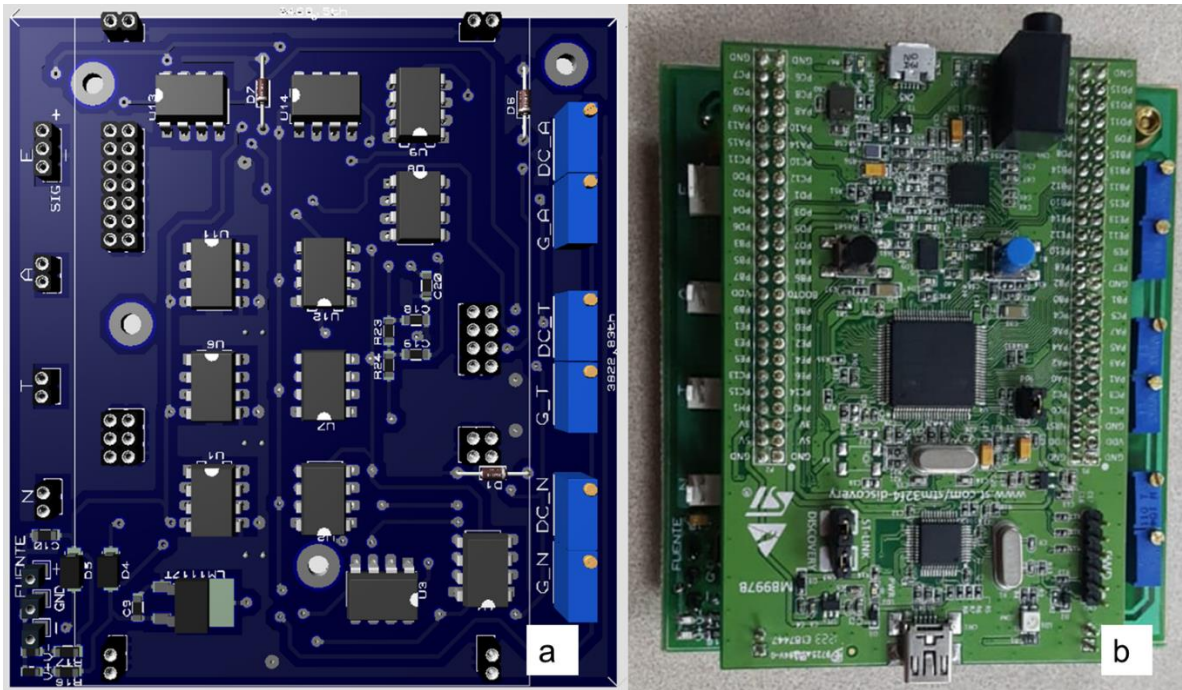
a) Renderizado del diseño de la segunda versión de la tarjeta real, b) Vista real de la tarjeta implementada con STM32 anclada en la parte superior.
